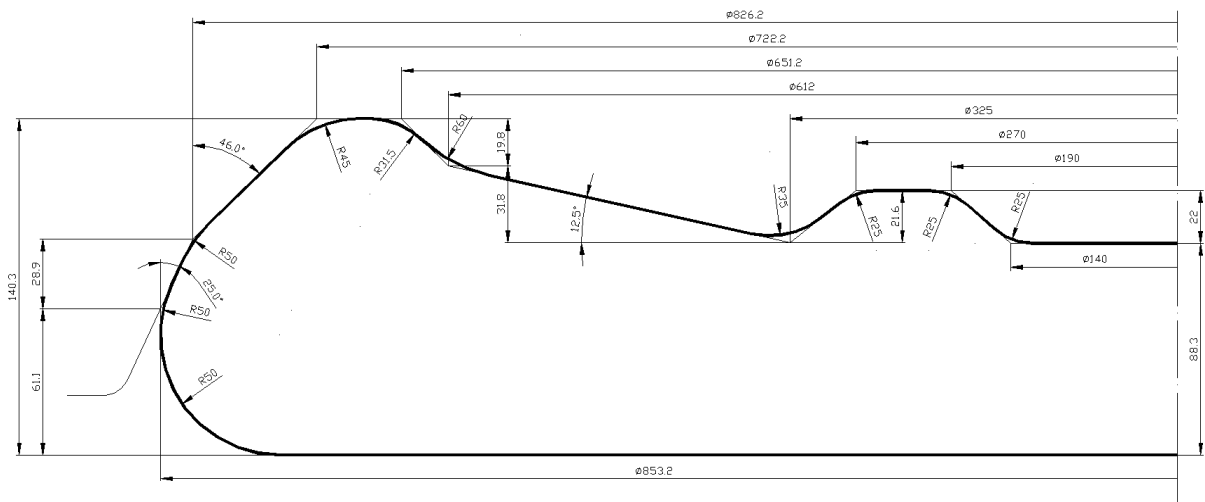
Контур сечения заготовки, полученной после выполнения операций осадки и разгонки исходной заготовки
